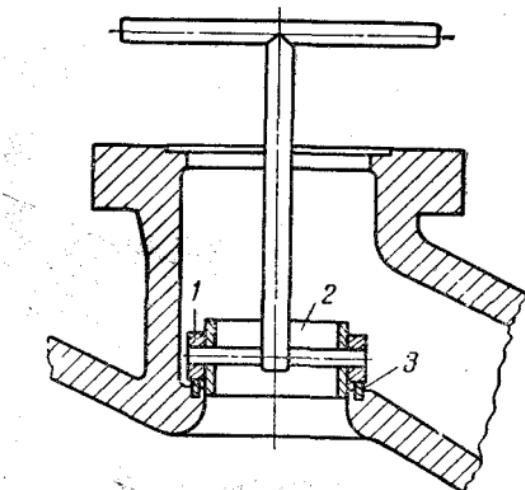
Приспособление для притирки уплотняющих поверхностей арматуры вручную
